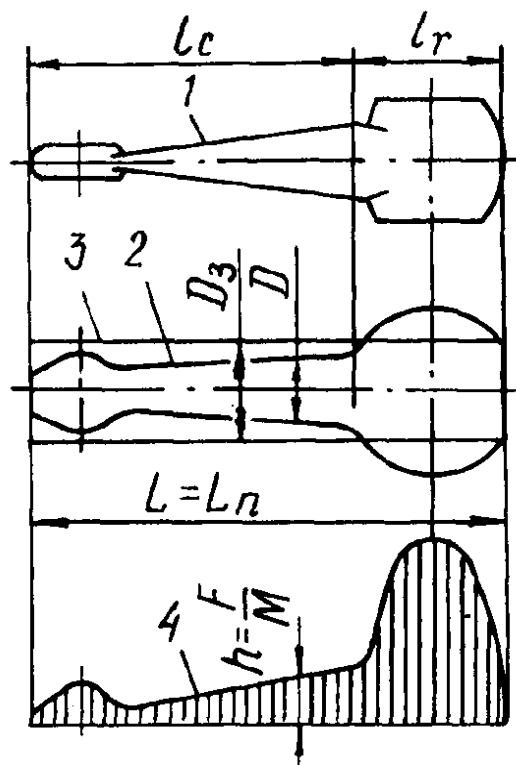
Елементарна розрахункова заготовка та епюра її перерізів :
